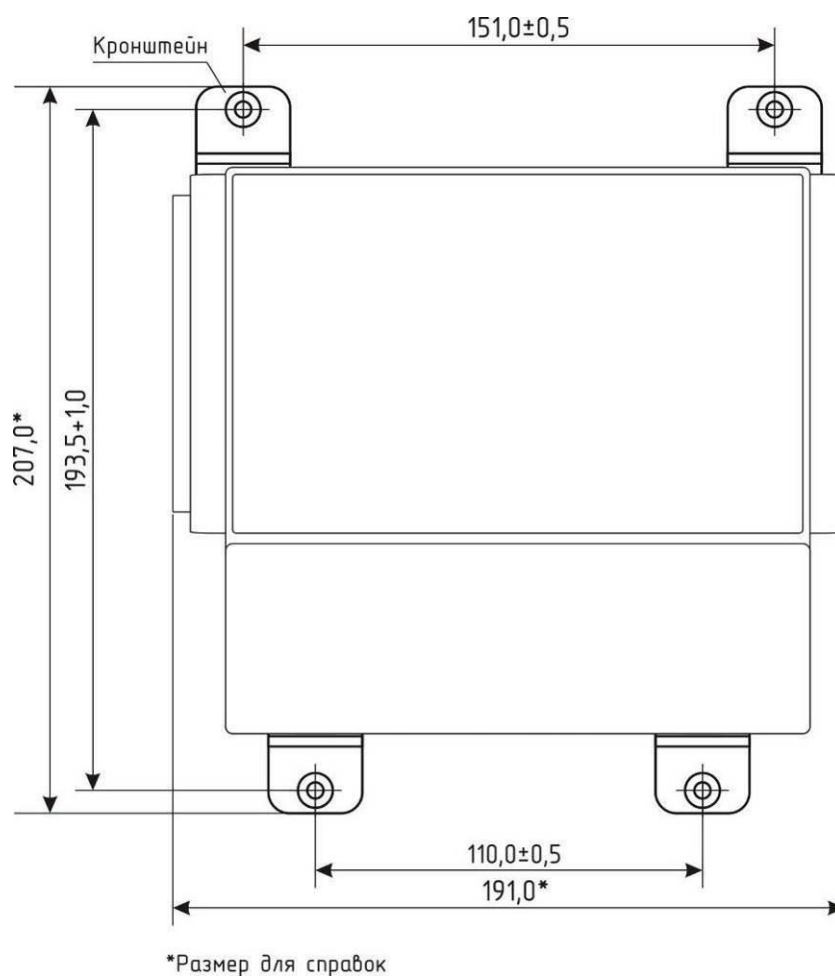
Разметка отверстий для крепления БСУ-КЕ
